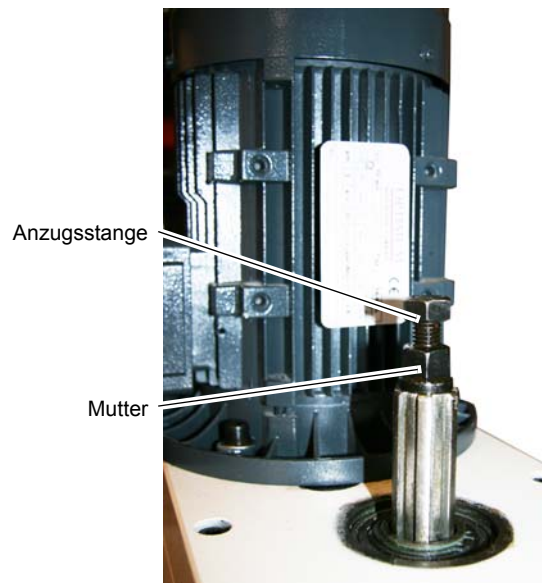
Bohr- Fräskopf ohne Abdeckkappe Anzugsstange
